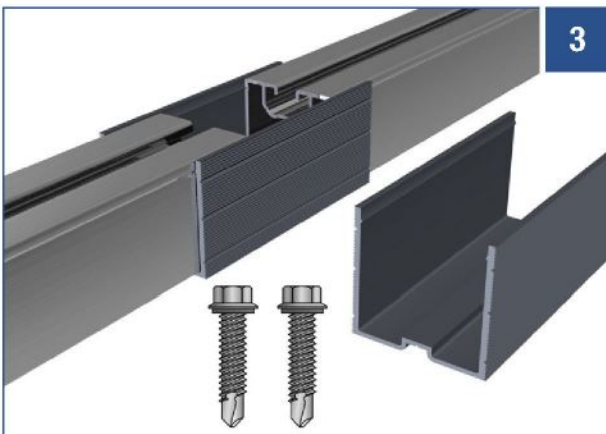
Enganchar la pieza de unión (PROFINESS 12) en el primer carril de montaje y encastrar en
